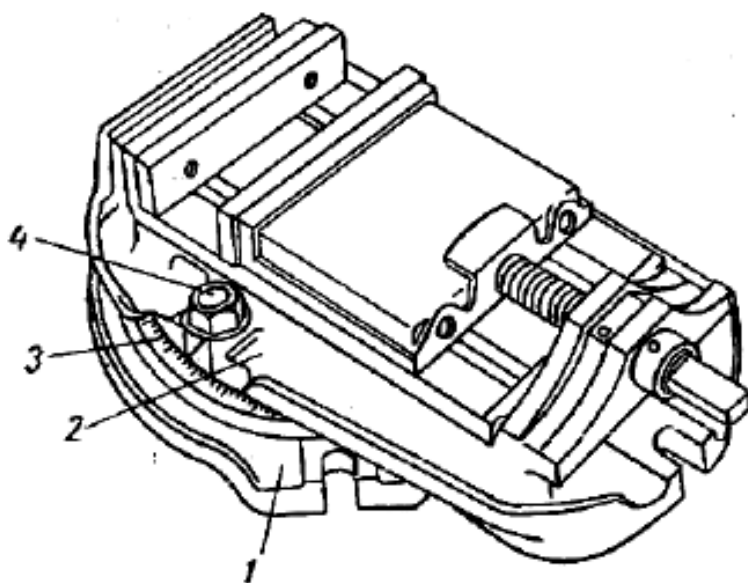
Поворотні лещата: 1 – плита; 2 – поворотний корпус; 3 – шкала; 4 – болт
